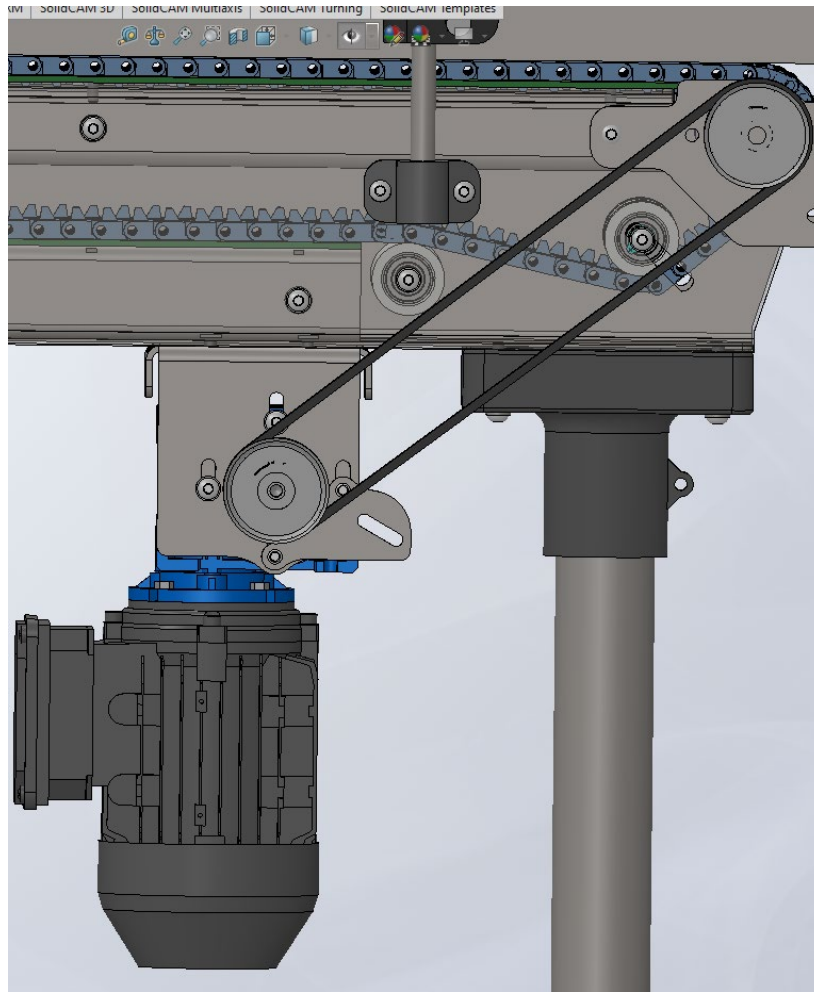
Зовнішній вигляд приводно-натяжного вузла
